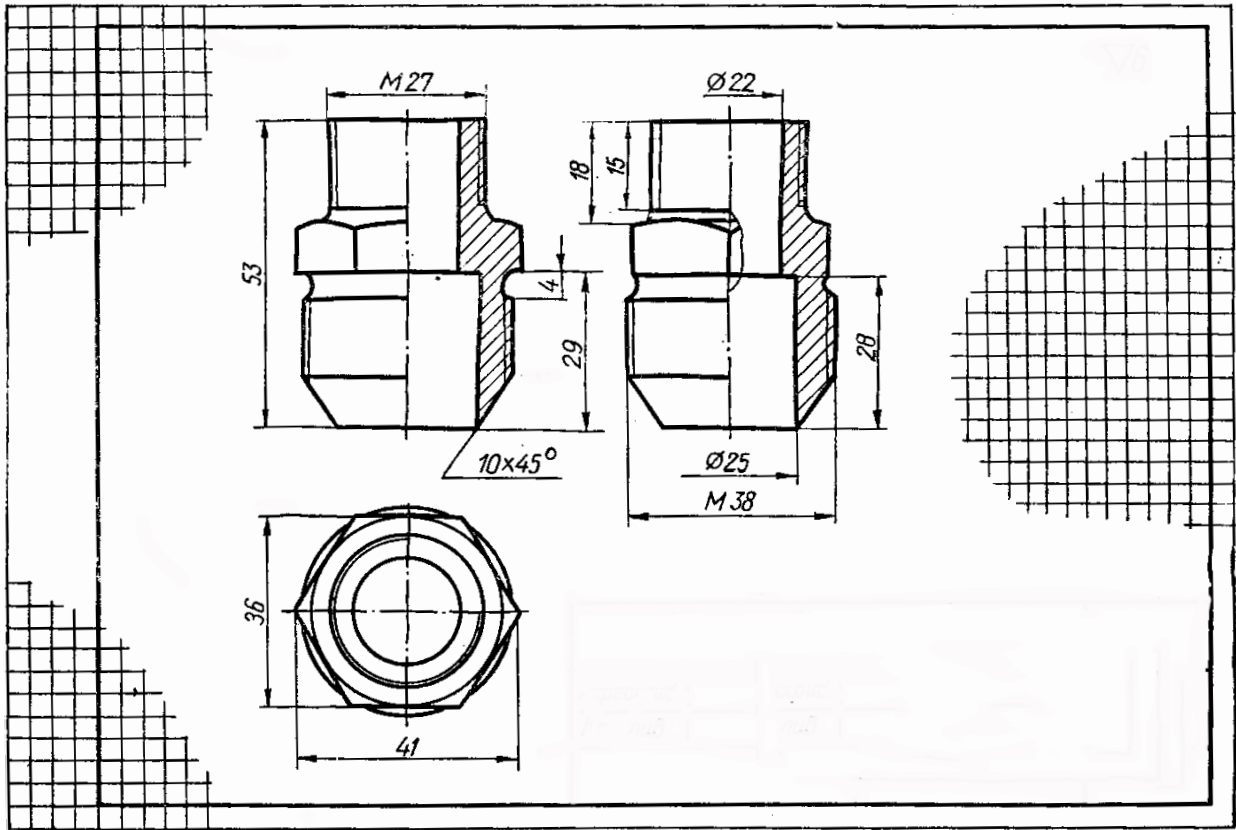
Ескіз деталі ізометрія якої виконується
